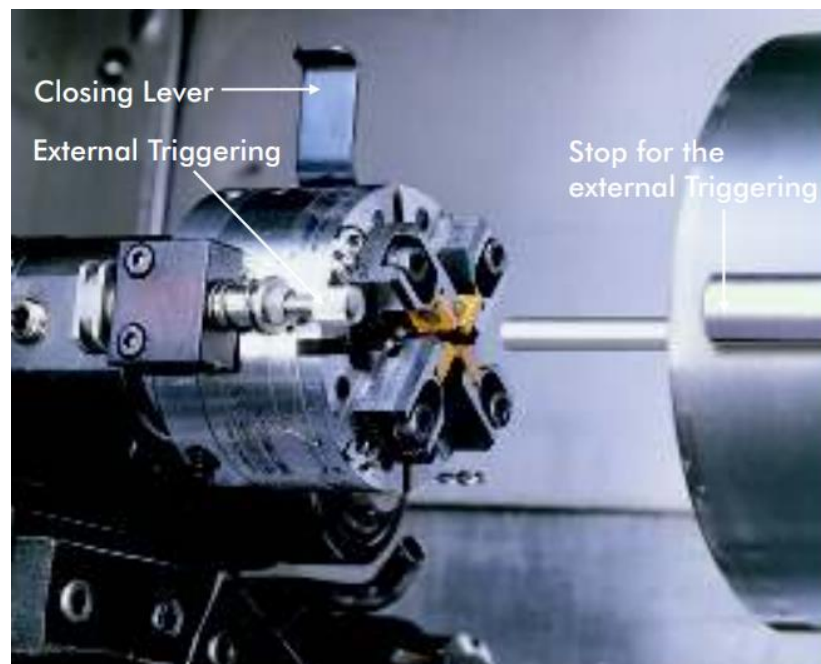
Багаторіцева токарна головка WAGNER [24]
